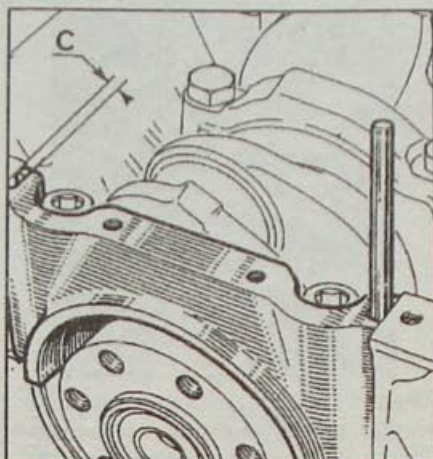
Место (С) измерения паза для выбора толщины уплотнительной прокладки крышки коренного подшипника №1
